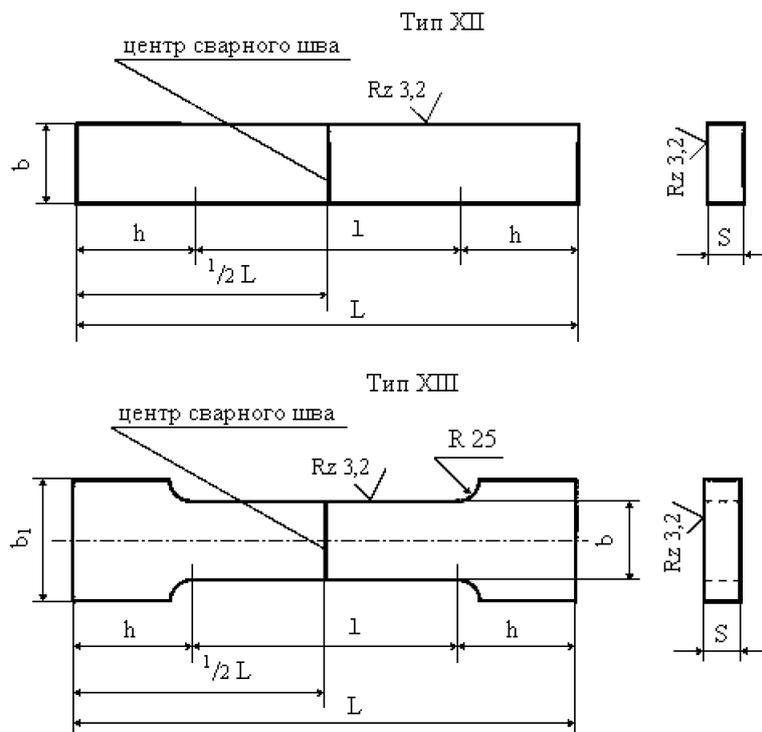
Форма образцов (тип XII и XIII) для испытаний сварного соединения на статическое растяжение
